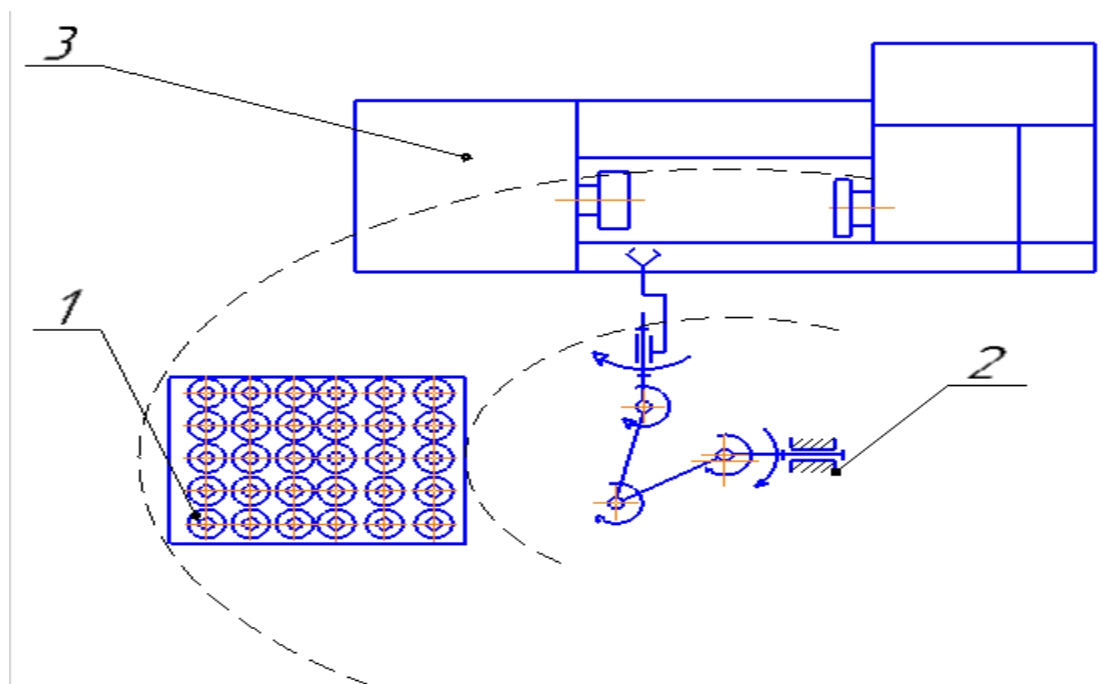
Схема автоматизированной ячейки токарного станка с ЧПУ:
